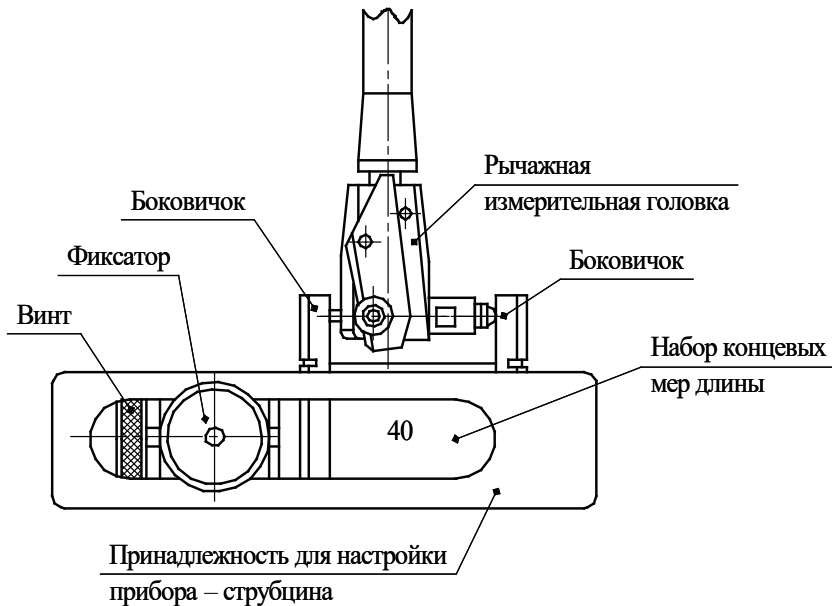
Подготовка струбины для настройки индикаторного нутромера
